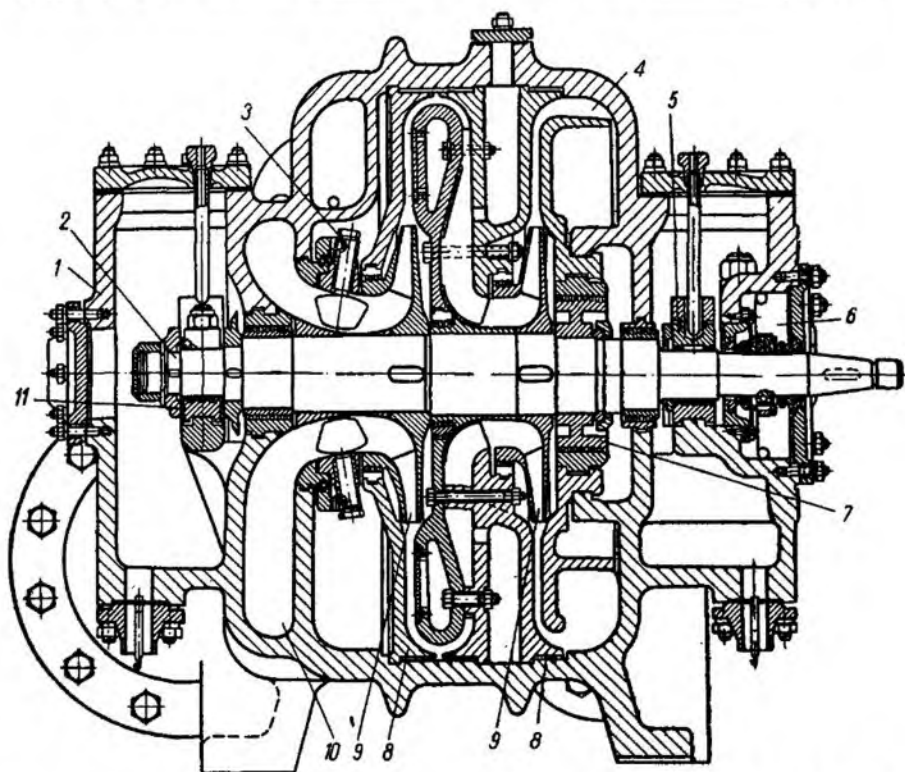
Фреоновый двухступенчатый центробежный компрессор ТКФ-2—48:
